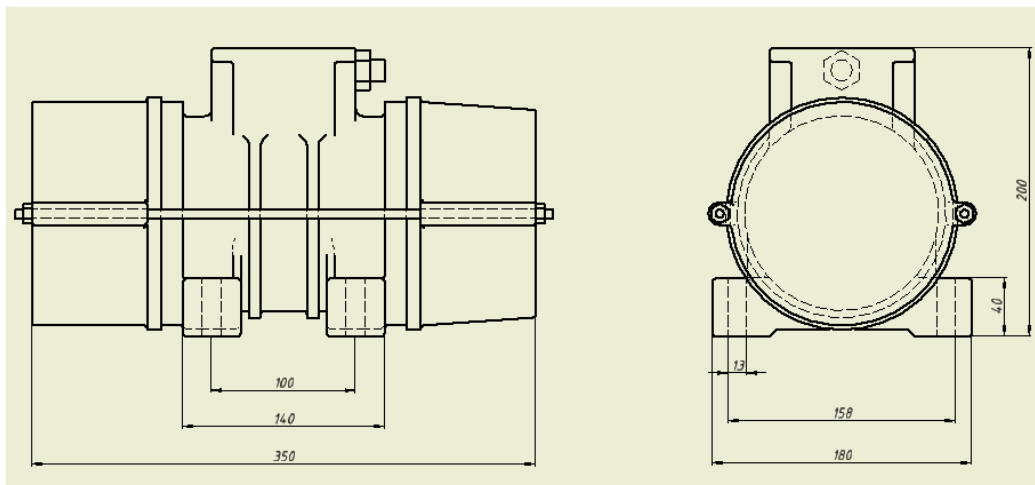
Схема електромеханічного вібратора ИВ-127
